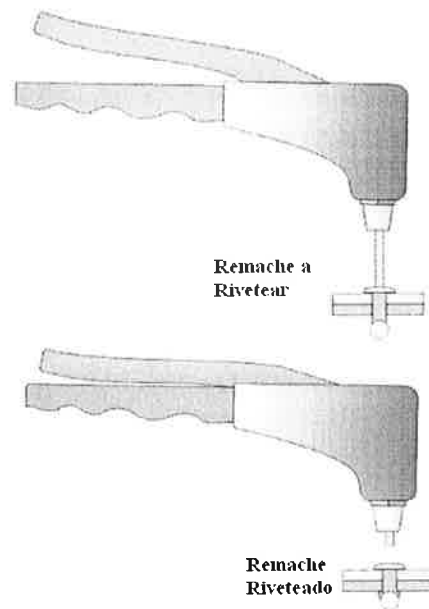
Riveteado de remache ciego con herramienta manual.
